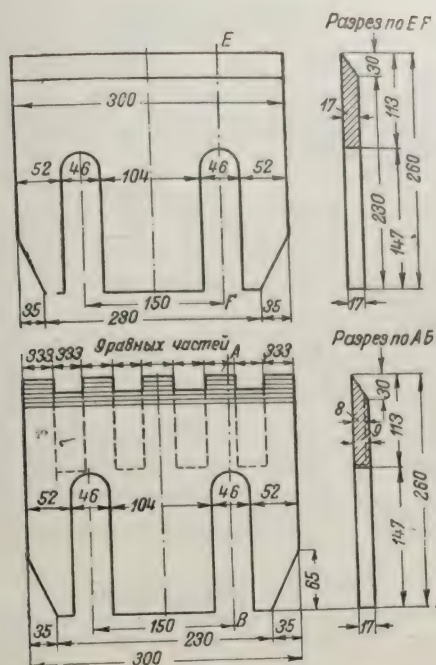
Гладкие и фрезерные ножи для рубильного станка РСА
